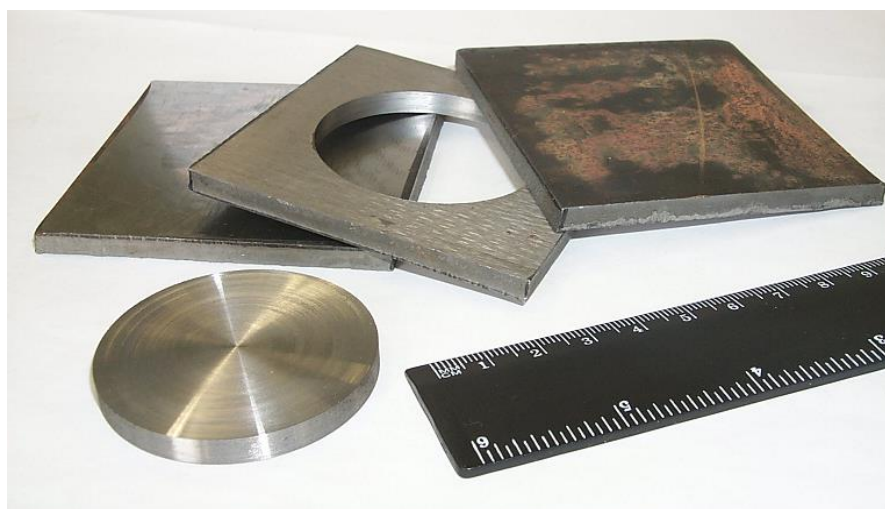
Внешний вид исходной заготовки и стальной оболочки
